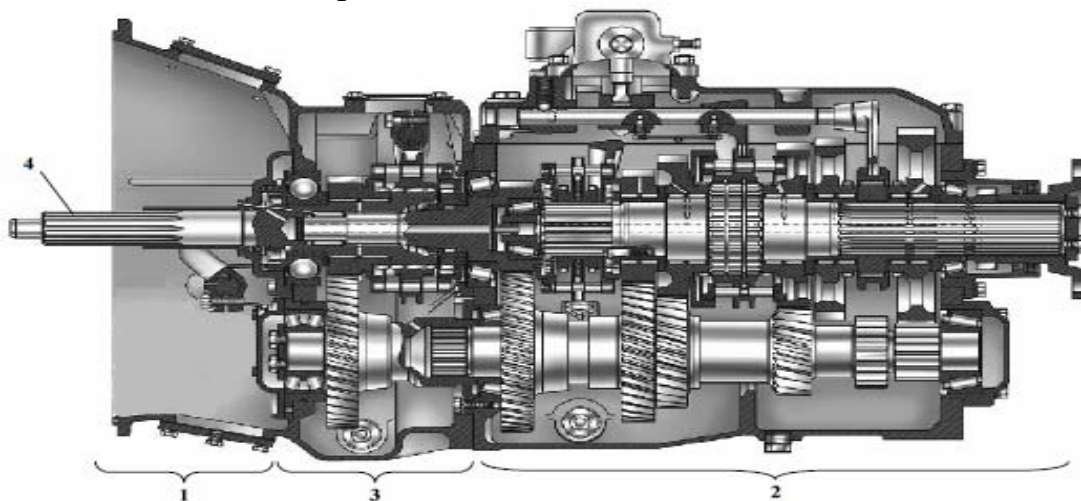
Конструкция десятиступенчатой коробки передач КАМАЗ модели 154: 1 – картер сцепления; 2 – основная трехвальная пятиступенчатая коробка передач; 3 – делитель; 4 – первичный вал делителя
